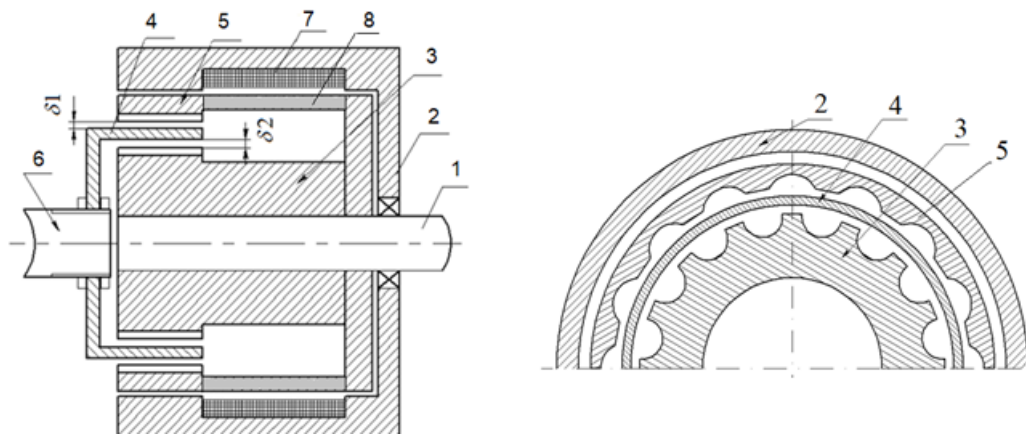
Конструкция электромагнитной гистерезисной муфты: 1 – ведущий вал; 2 – наружный индуктор; 3 – внутренний индуктор; 4 – гистерезисный слой; 5 - внешний индуктор; 6 – ведомый вал; 7 – неподвижная обмотка возбуждения; 8 – немагнитная вставка;  $\delta 1$ ,  $\delta 2$  - рабочие зазоры.
